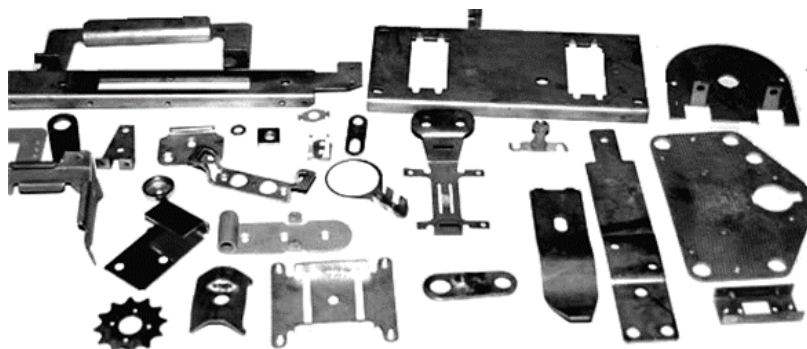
Деталі, які виготовлені методом холодного листового штампування
